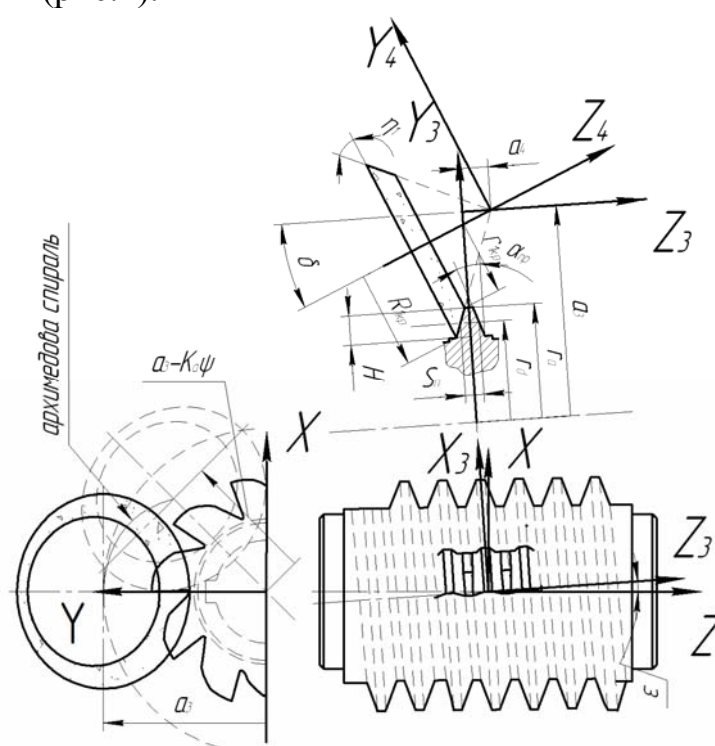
Образование задней затылованной поверхности зуба фрезы
